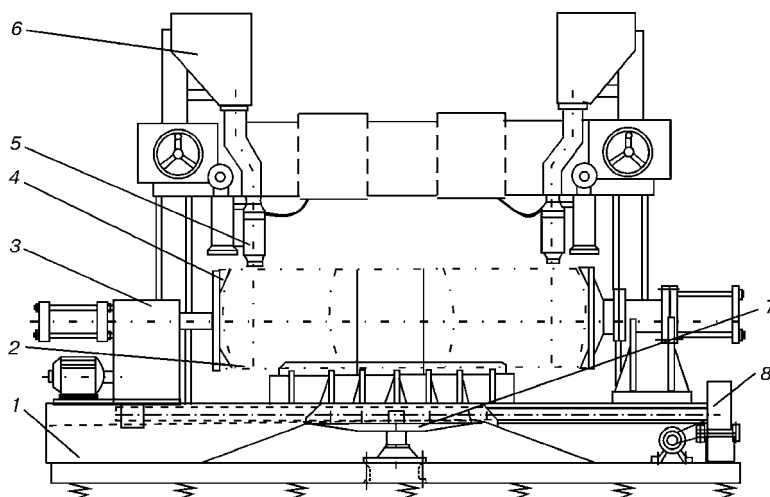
Схема специализированной установки для сварки под слоем флюса одновременно двух кольцевых швов: 1 — станина; 2 — резервуар; 3 — привод вращения резервуара; 4 — захват; 5 — сварочная головка; 6 — бункер для флюса; 7 — стол подъемный; 8 — привод поднятия резервуара
